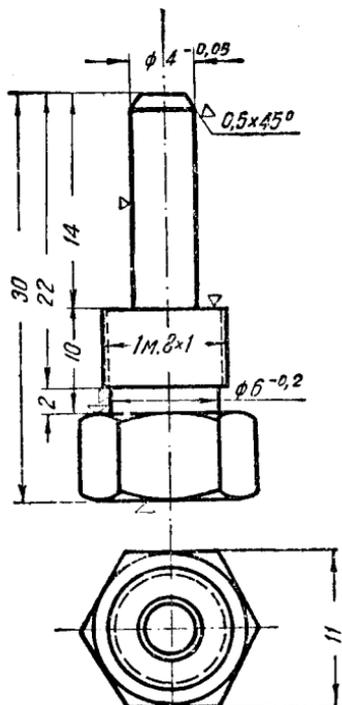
Дет. № 327. Ось рычага поплавка для топлива и воды
